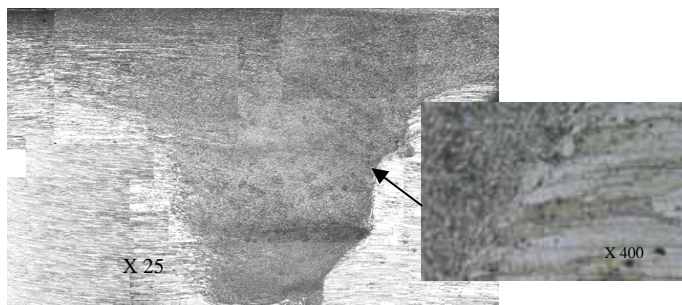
Макро- и микроструктура поперечного сечения сварного шва, выполненного СТП.
